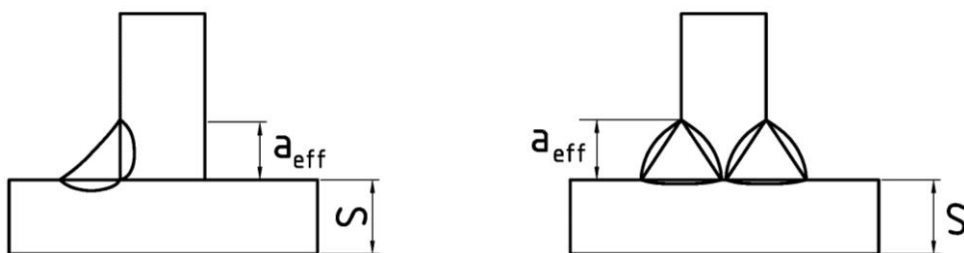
Эффективный катет сварного шва a_{eff} для усадки
